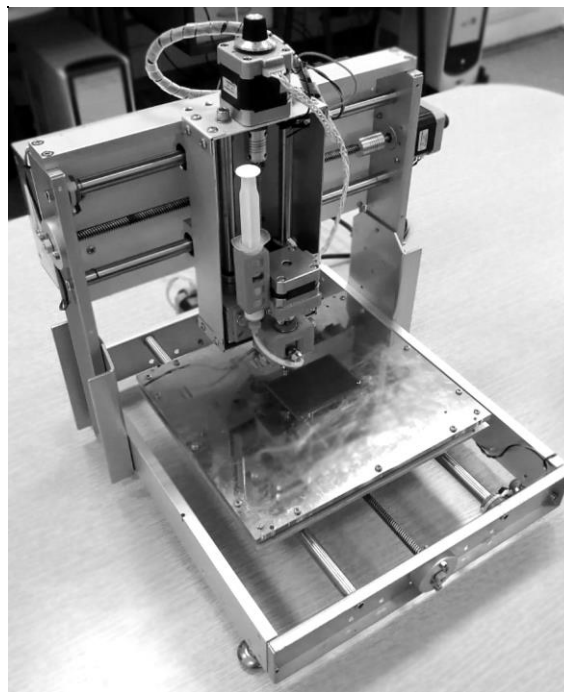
Внешний вид установки для изготовления многослойных печатных плат
